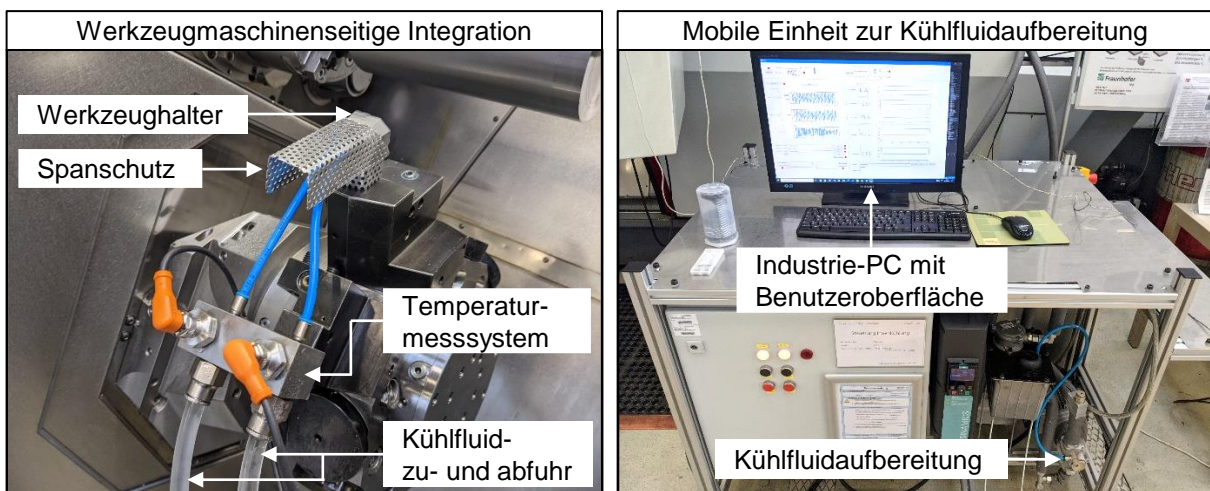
Integration des innengekühlten Werkzeugsystems am IWF
